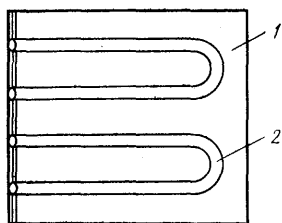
Листотрубный конденсатор со свободным движением воздуха:
